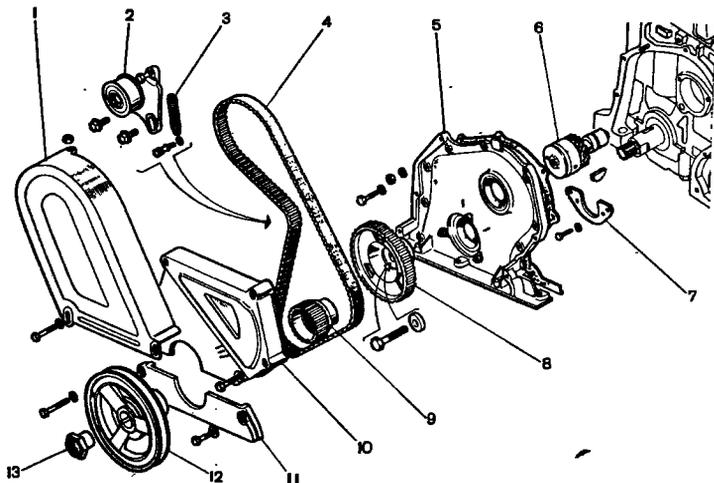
Разборка передней части двигателя: 1 - верхняя защитная крышка; 2 - натяжной ролик; 3 - натяжная пружина; 4 - ремень привода распределительного вала; 5 - крышка привода распределительного вала; 6 - валик привода масляного насоса и распределителя зажигания; 7 - упорный фланец; 8 - шкив валика привода масляного насоса; 9 - зубчатый шкив коленчатого вала; 10 - средняя защитная крышка; 11 - нижняя защитная крышка; 12 - шкив привода генератора и насоса охлаждающей жидкости; 13 - гайка
